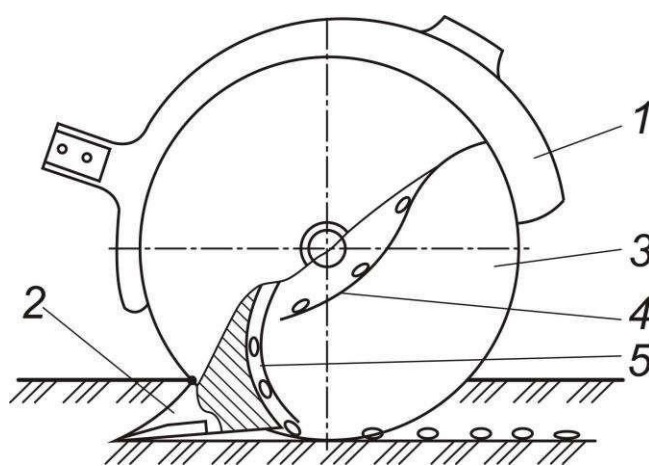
Дисківий сошник зі стабілізатором: 1 – корпус; 2 – розпушувач; 3 – диск; 4 – направляючий; 5 – ребро
